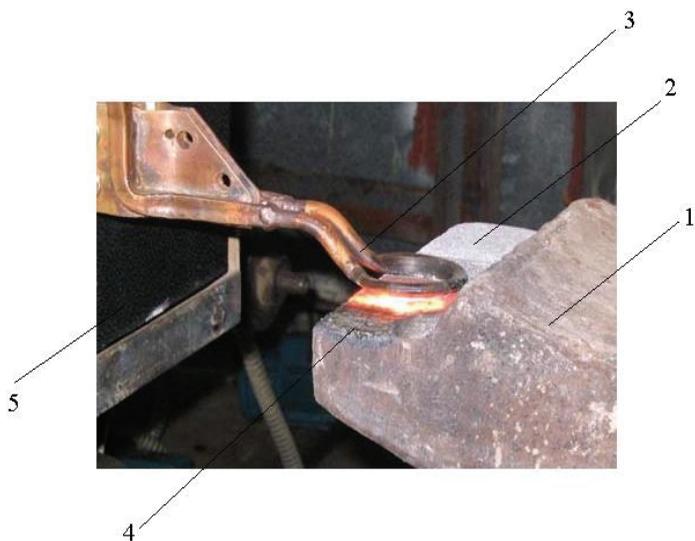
Наплавка опорной плиты петлевым индуктором:
